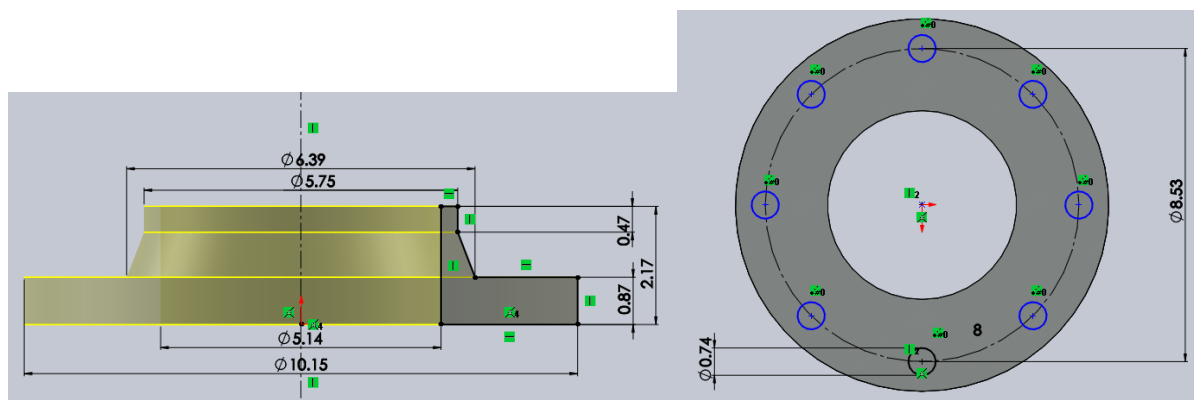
Dimensionamiento de las bridas de cuello soldable para el intercambiador de calor. Fuente: SolidWorks
